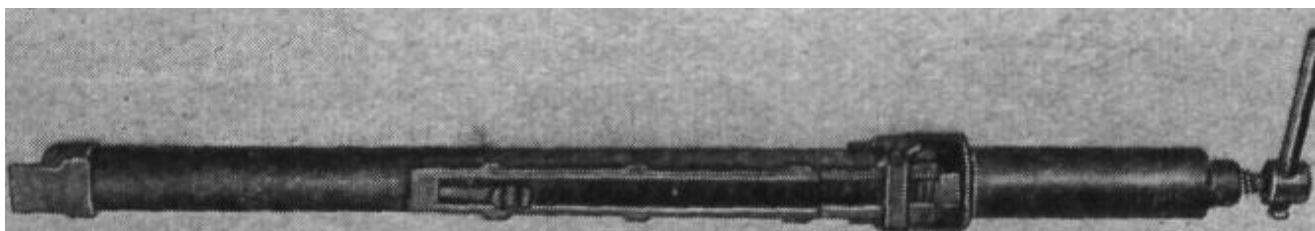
Присоединение к механизму перезарядки приспособления для его разборки
